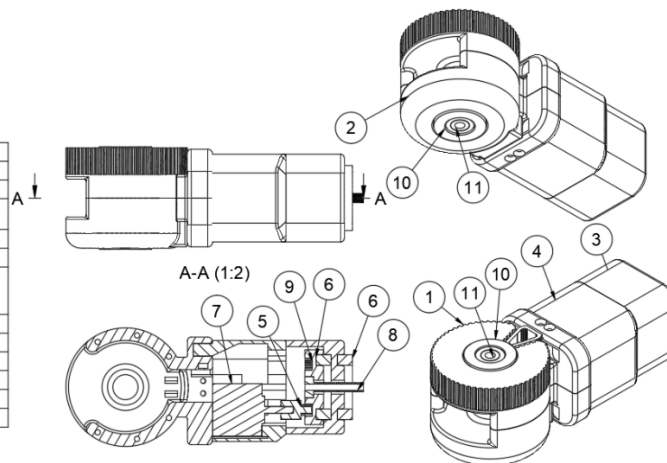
Zaprojektowana konstrukcja przegubu numer 3.
